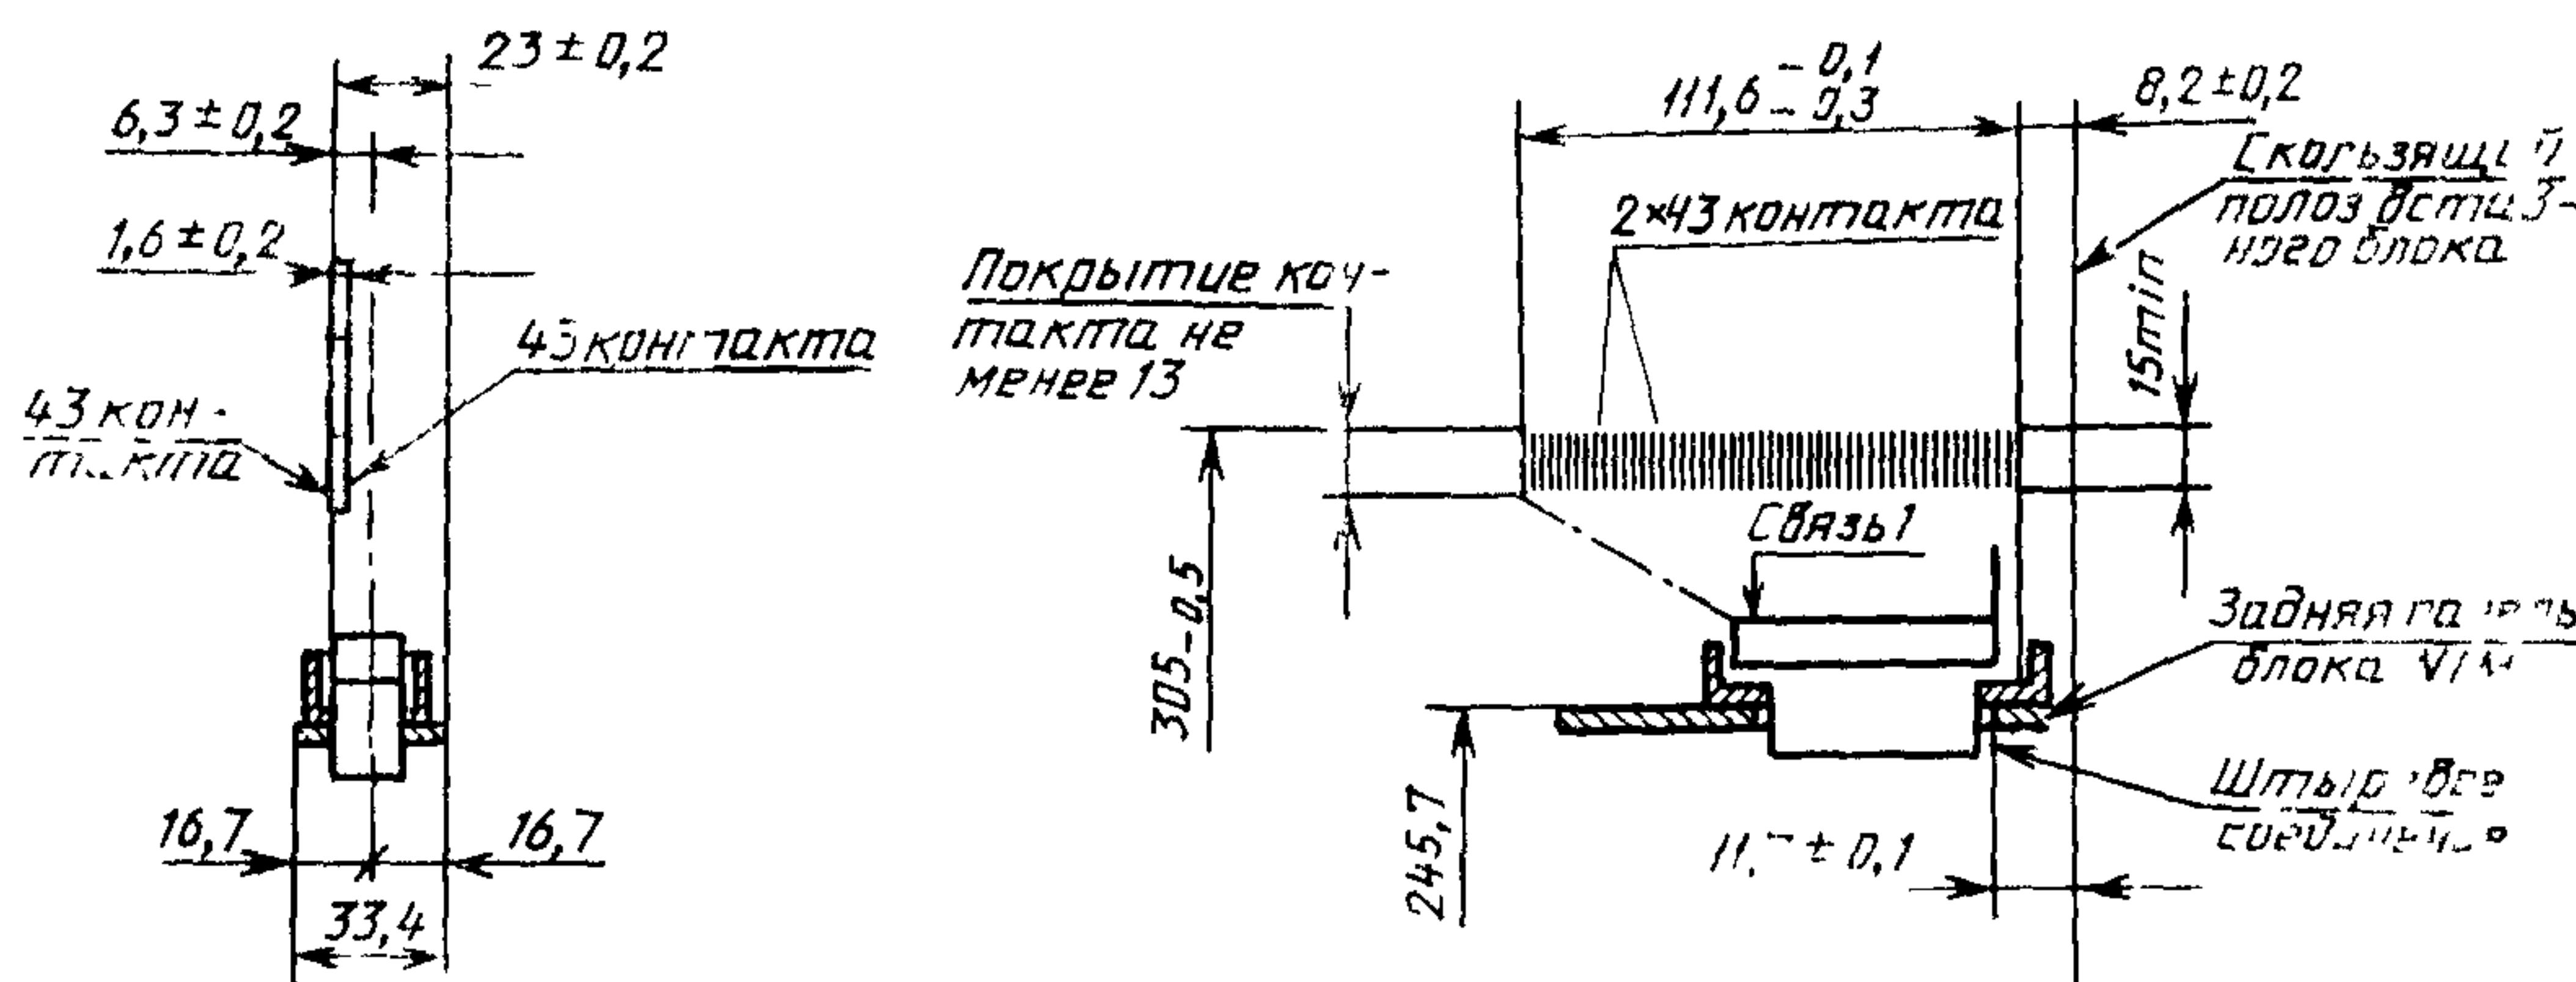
Соединитель магистрали вилка (5.1—5.3) — розетка (5.4—5.8)
